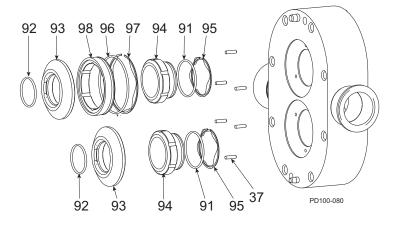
Simple (bas) et double (haut) Joint mécanique
